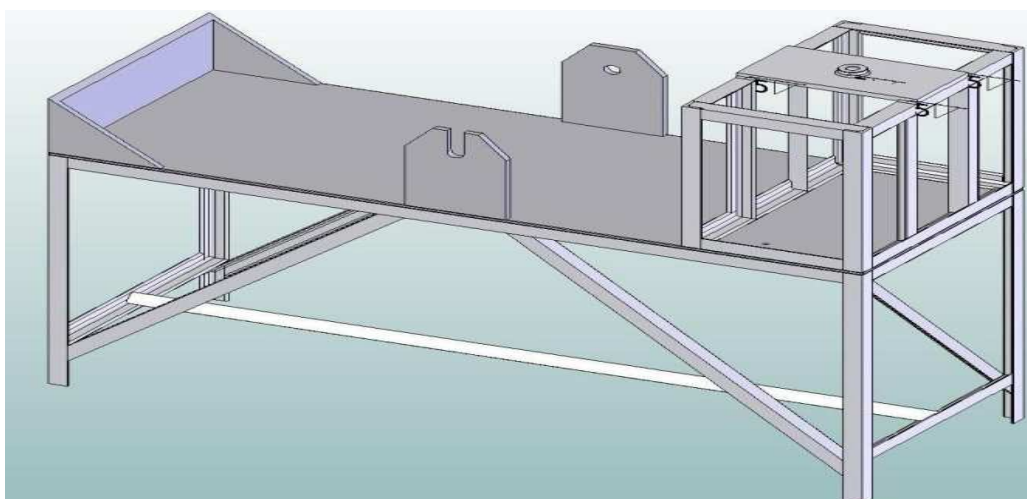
Mesa do dispositivo de ensaio de CST sob carga constante.
